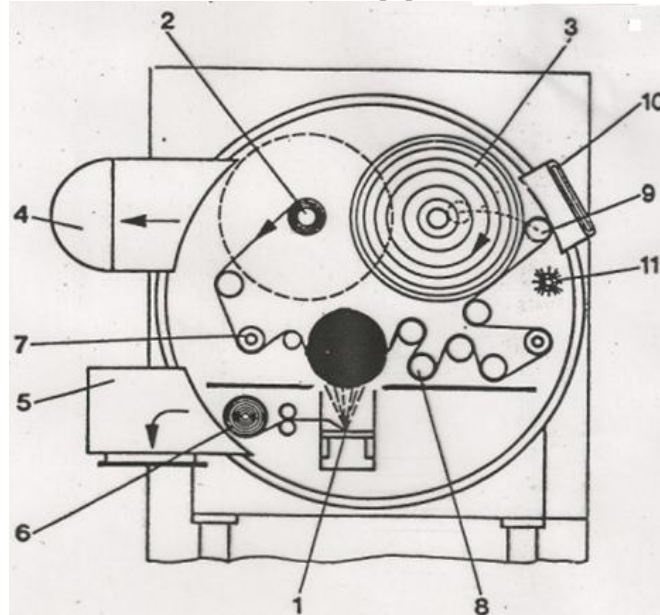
Principais elementos de uma metalizadora a vácuo para embalagens de alimentos: (1) cadinho cerâmico para evaporação do alumínio; (2) cilindro desbobinador de filme não metalizado; (3) cilindro embobinador do filme metalizado; (4) bomba de vácuo; (5) bomba difusora de alto vácuo; (6) fio de alumínio; (7) cilindros de passagem; (8) cilindros de refrigeração. Fonte [2].
